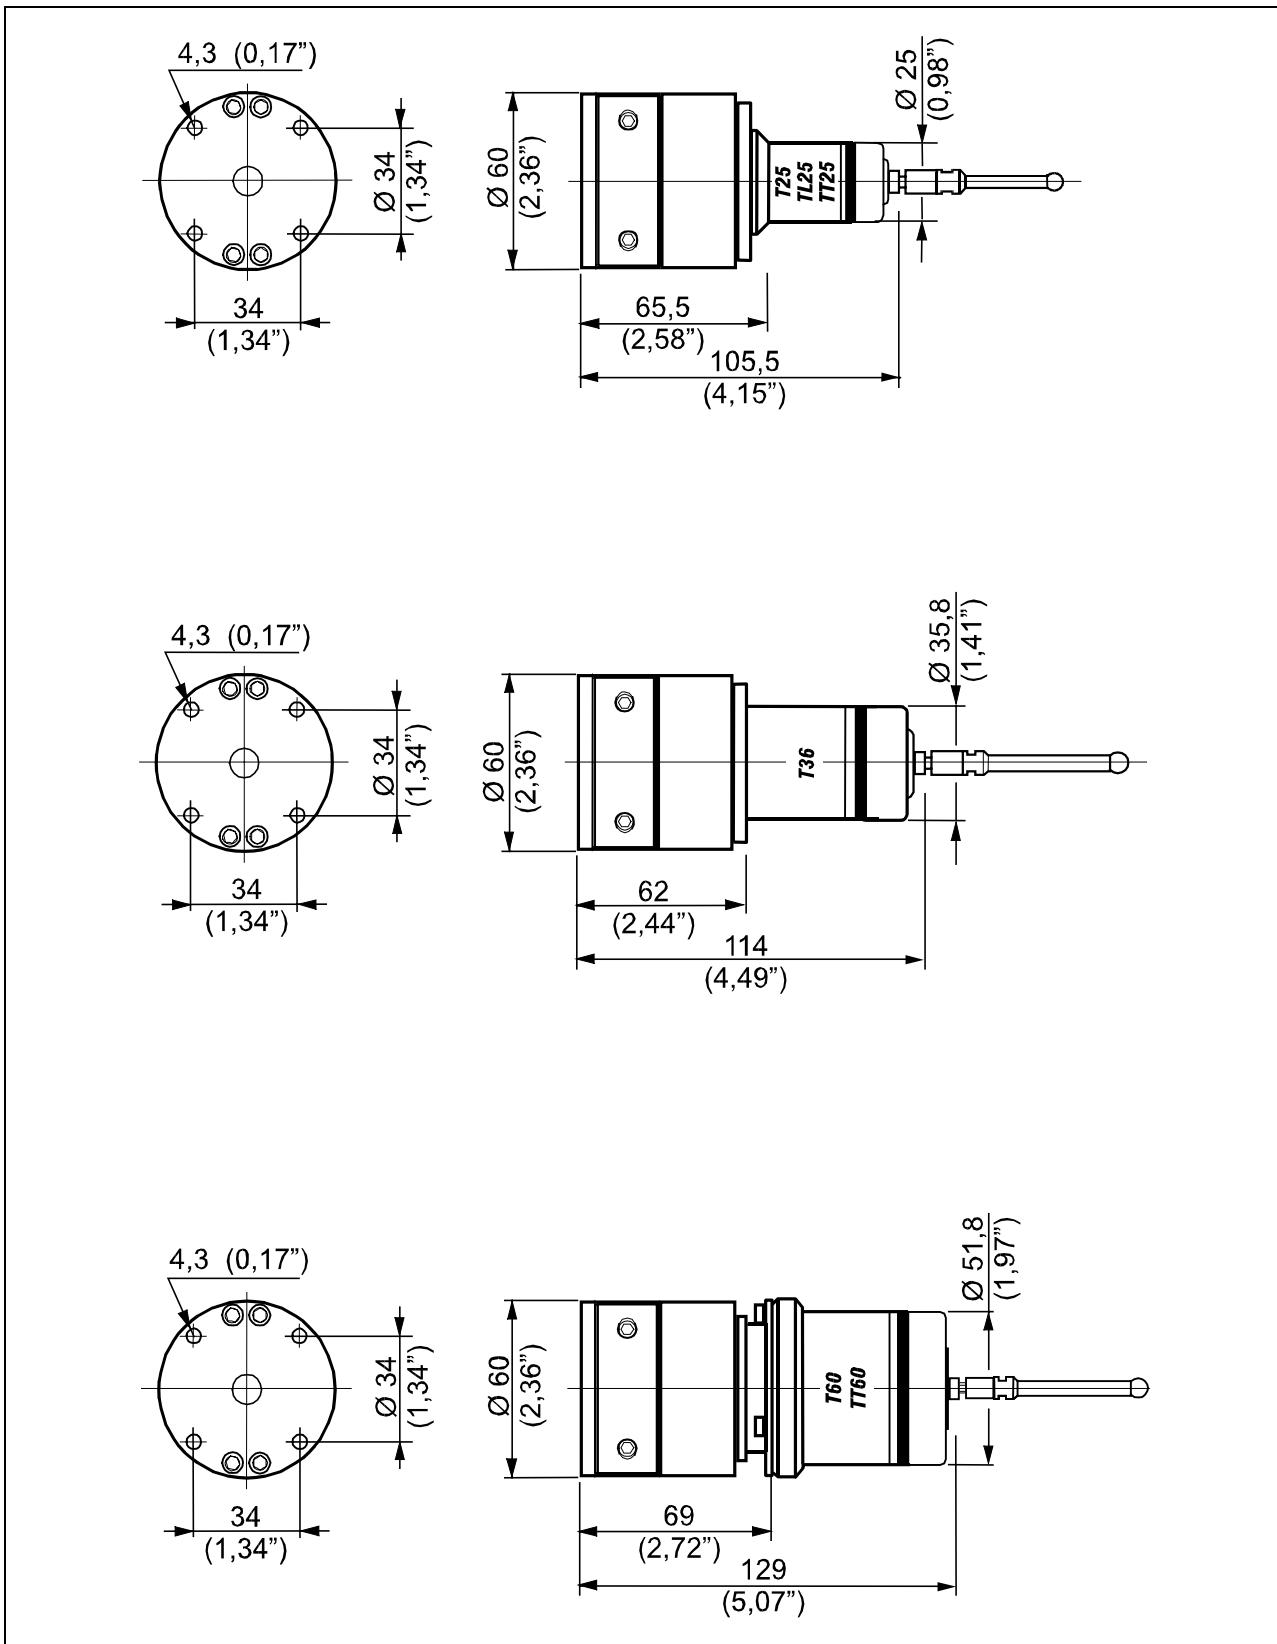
Dimensions hors tout émetteur avec flasque standard
